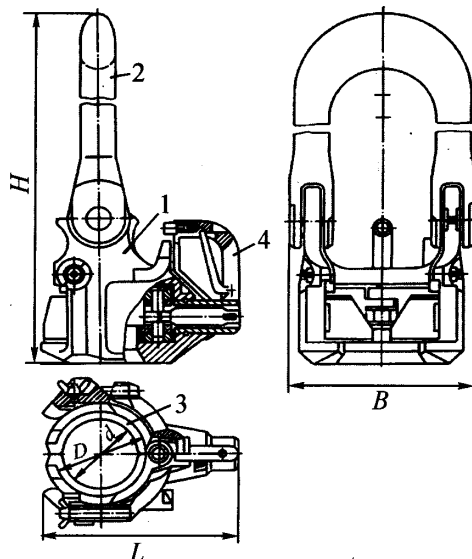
Элеватор ЭТА: 1 – корпус; 2 – серьга; 3 – сменные захваты для труб; 4 – рукоятка
